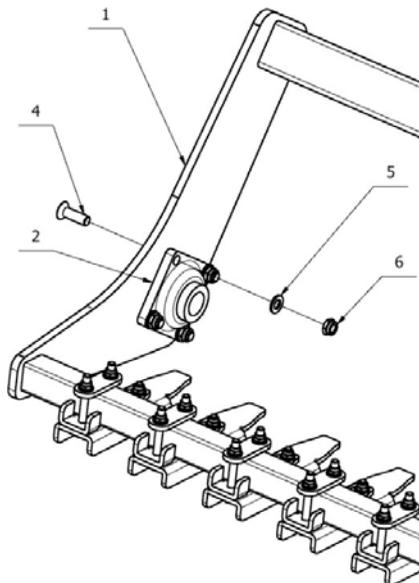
Dachwalze Ø500mm - Lagermontage.
